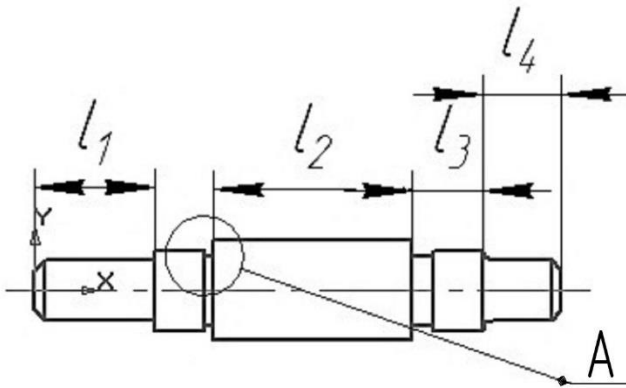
Конструкция вала редуктора с различными длинами шеек
